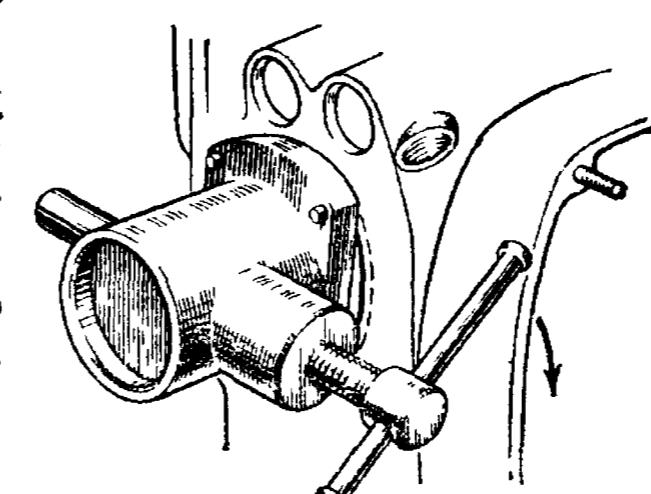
Выпрессовка поршневого пальца с помощью специального приспособления
